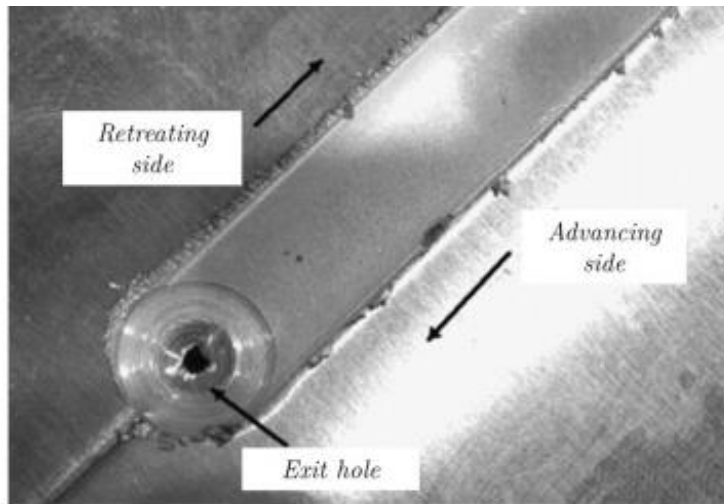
Saldatura tramite Friction Stir Welding
